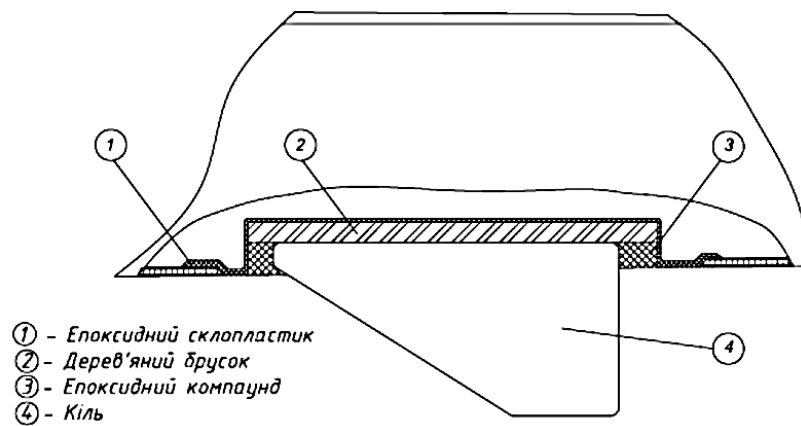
Схема розташування закладної деталі – бруса.
